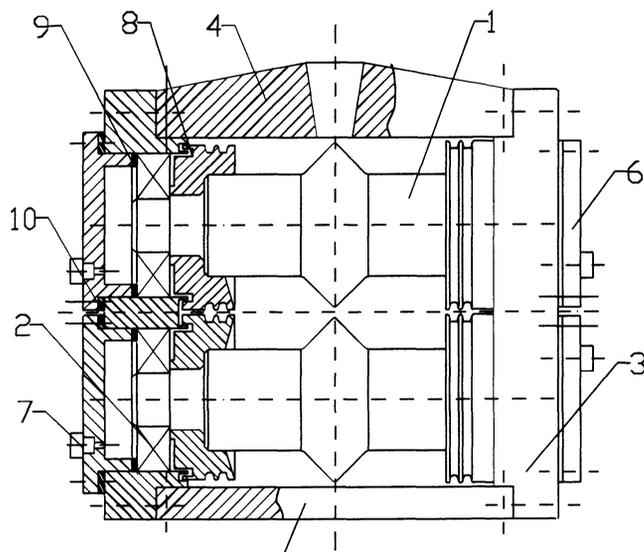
Конструкция делительного устройства ИЧМ НАН Украины: 1 – делительные ролики; 2 – подшипники; 3 – боковые стойки корпуса; 4 – крышка корпуса; 5 – основание корпуса; 6 – торцовые крышки; 7 – масленки; 8 – торцовые элементы лабиринтного уплотнения; 9 – прокладки
